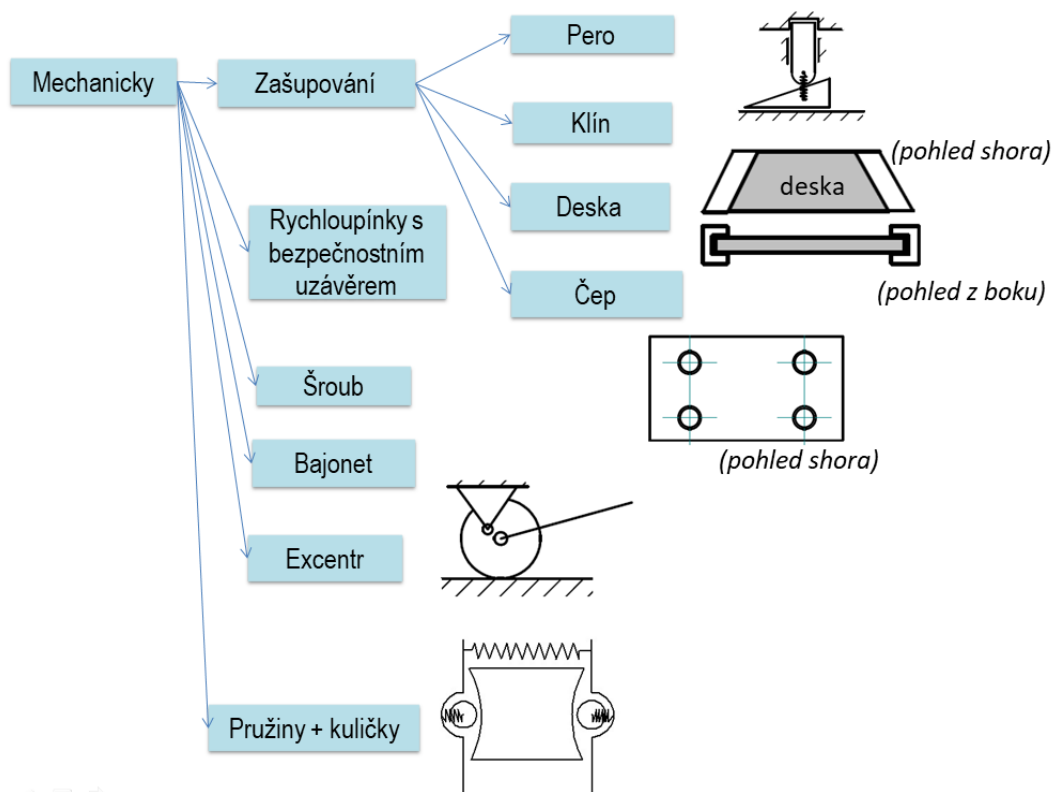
Přehled základních principů mechanismů použitelných ke upevnění boxu ke saním.
